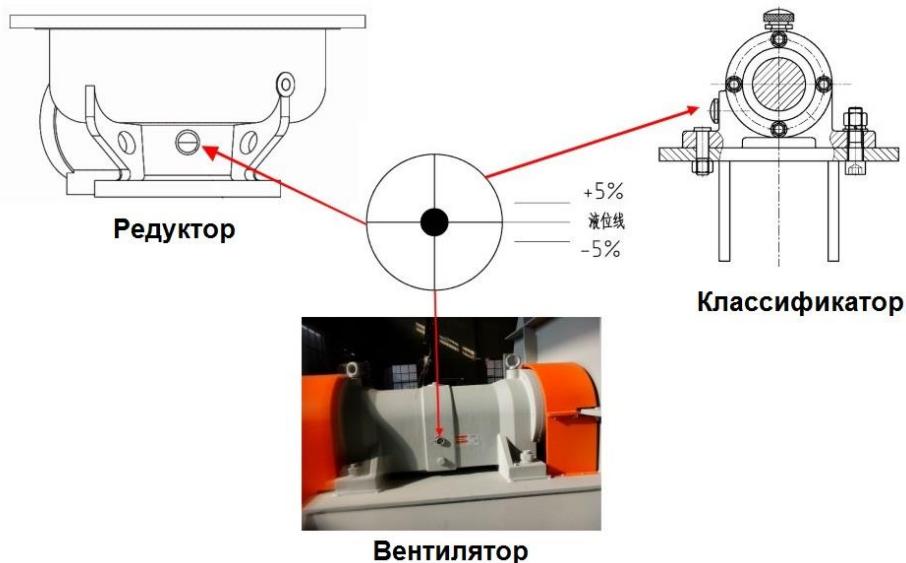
Точки смазки редуктора, классификатора, вентилятора
